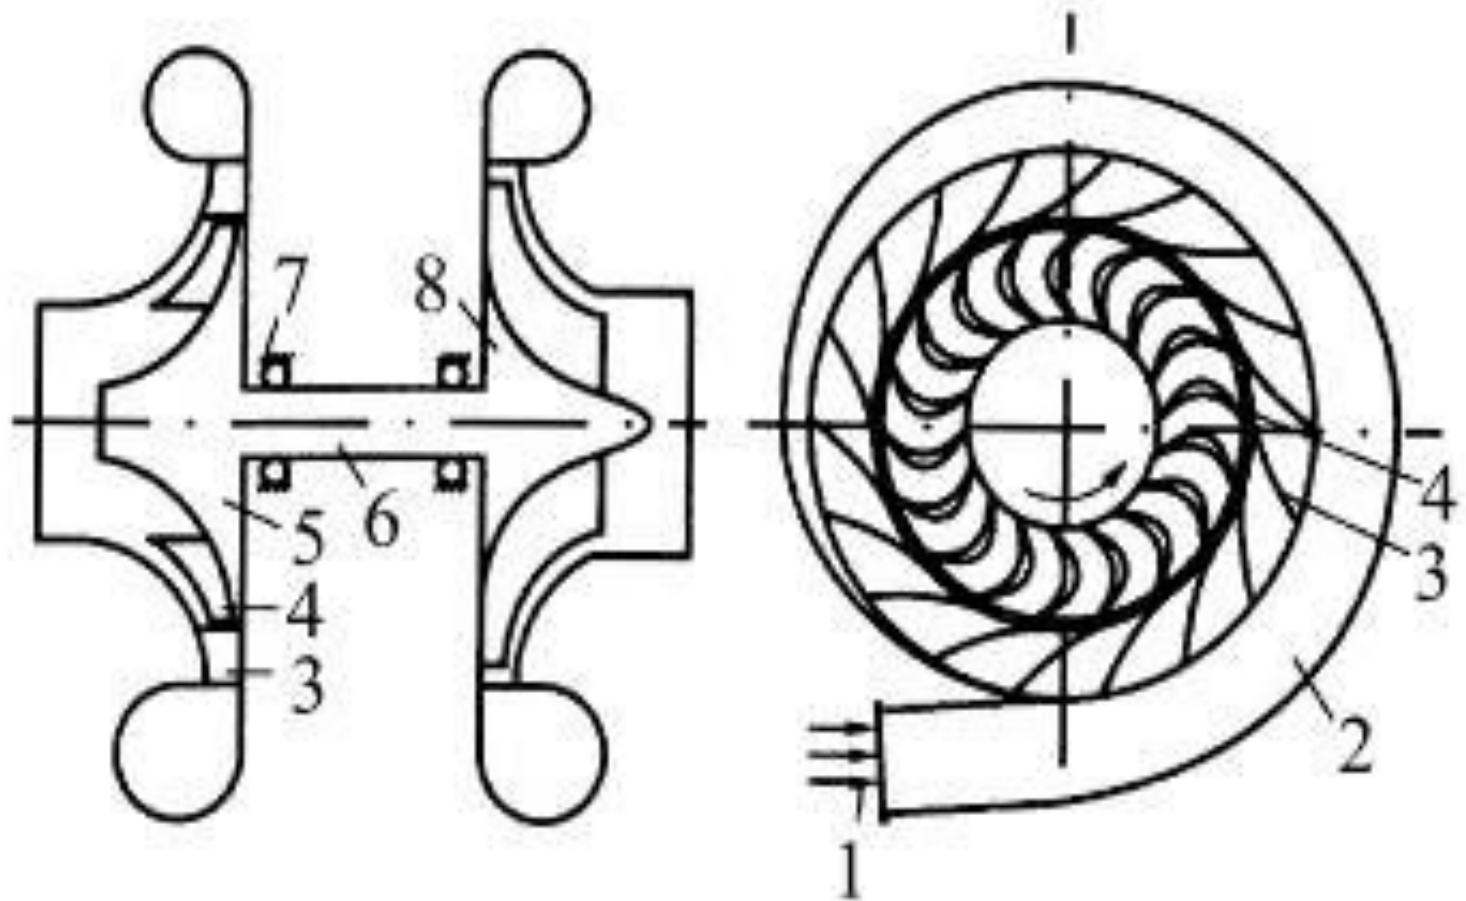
Принципиальная схема турбохолодильника [2]: 1 – патрубок, 2 – улитка, 3 – сопловой аппарат, 4 – лопатки рабочего колеса, 5 – рабочее колесо турбины, 6 – вал, 7 – подшипник, 8 – рабочее колесо вентилятора
